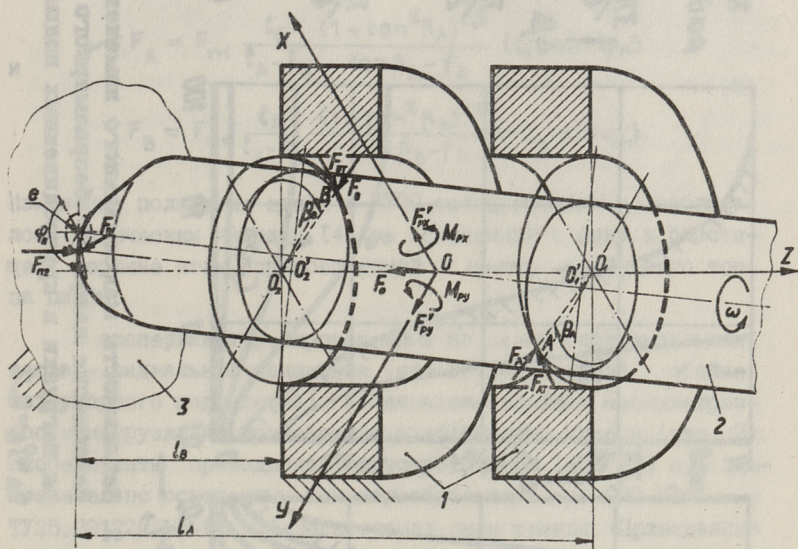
Схема совместной работы радиальных и упорных подшипников, 1 - цапфа; 2 - радиальный подшипник; 3 - упорный подшипник.
